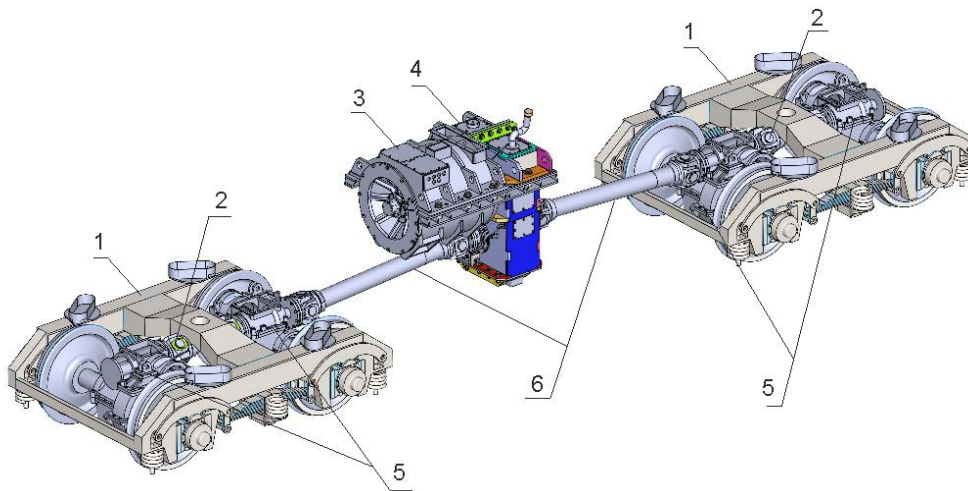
Схема приводу з центральним електричним мотор-редуктором та карданним приводом осьових редукторів тепловозу ТГМ6Д-МЕ: 1 – двовісний візок; 2 – вали карданні візкові; 3 – тяговий електричний двигун; 4 – тяговий редуктор; 5 – колісні пари з осьовими редукторами; 6 – карданні вали роздаткові
